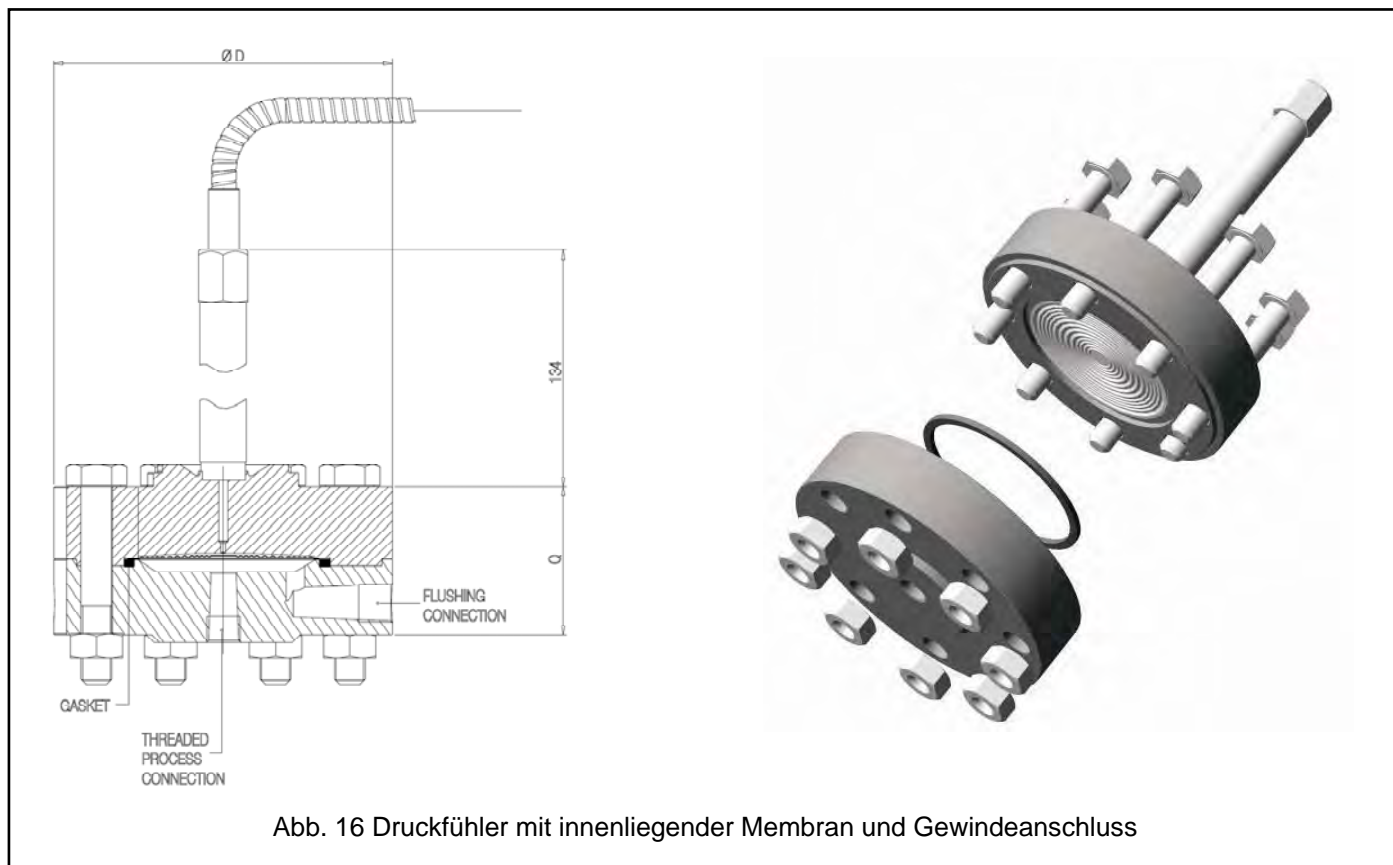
Druckfühler mit innenliegender Membran und Gewindeanschluss
